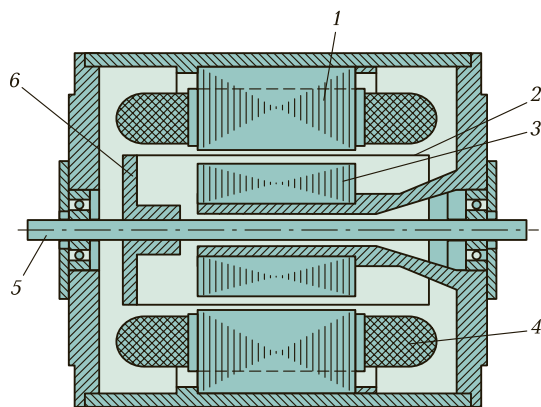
Асинхронный двигатель с полым немагнитным ротором:
